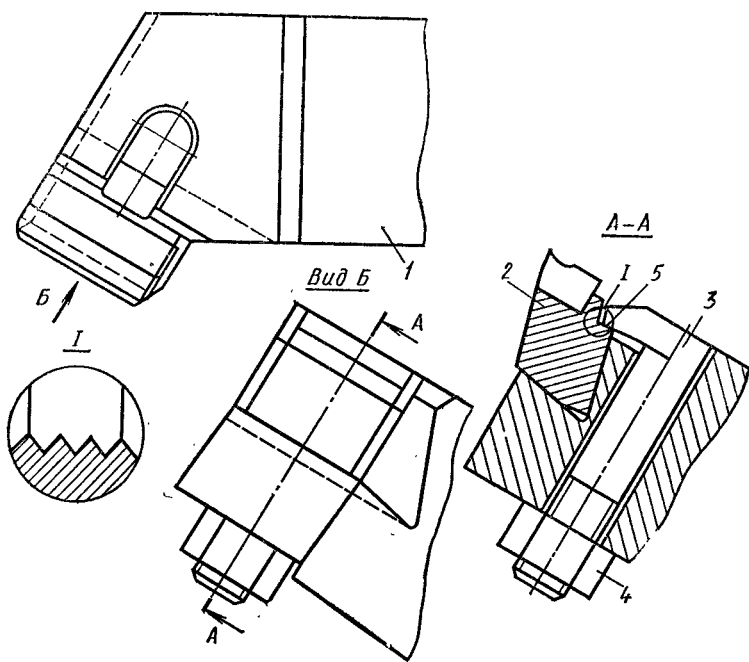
Сборный крупногабаритный резец (конструкции ВНИИ)
